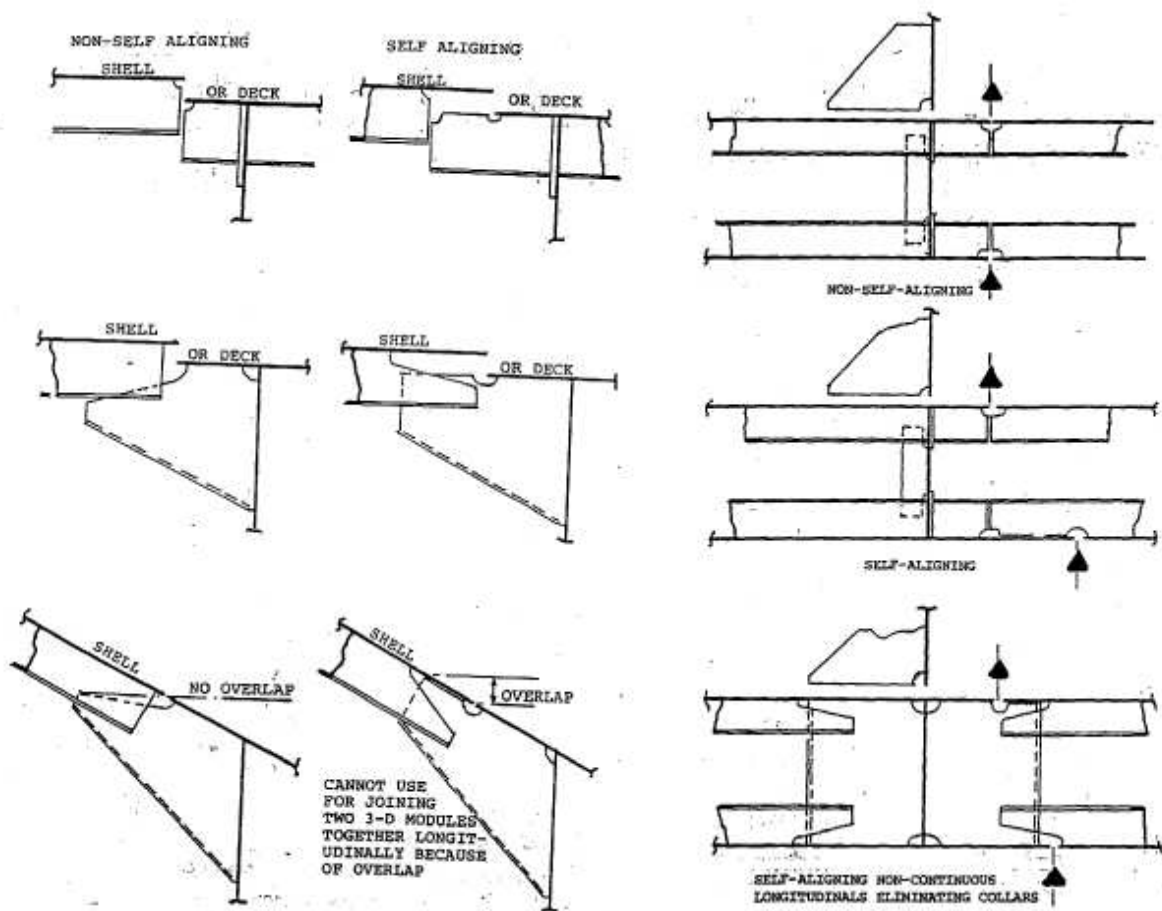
Ligação de detalhes estruturais e elementos resistentes longitudinais
